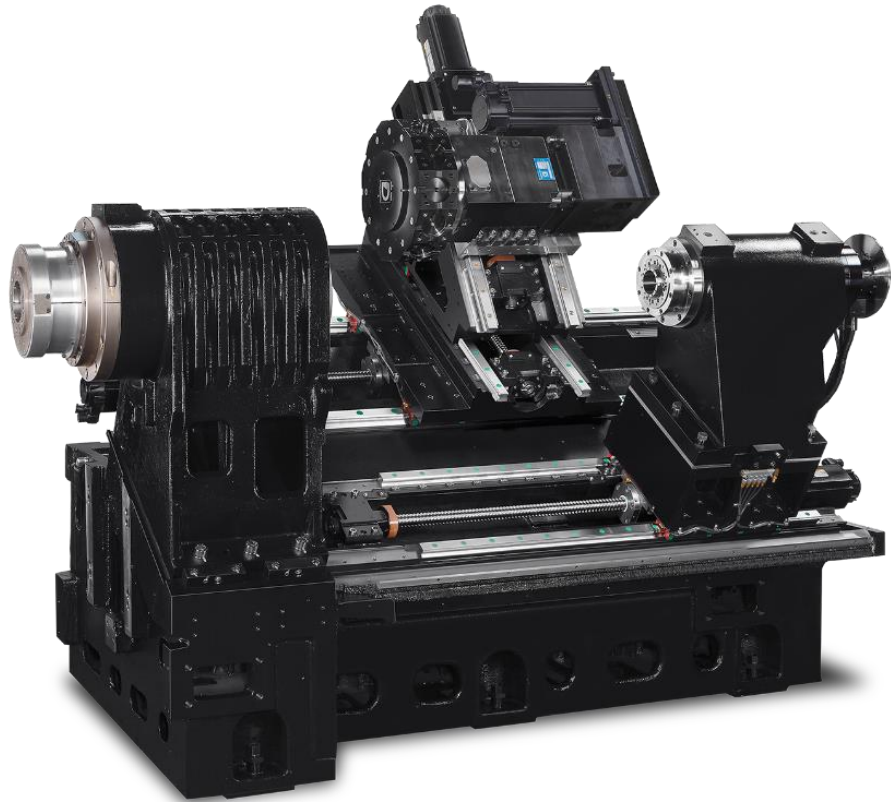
Компонування багатошпindelного токарного верстата з ЧПК
